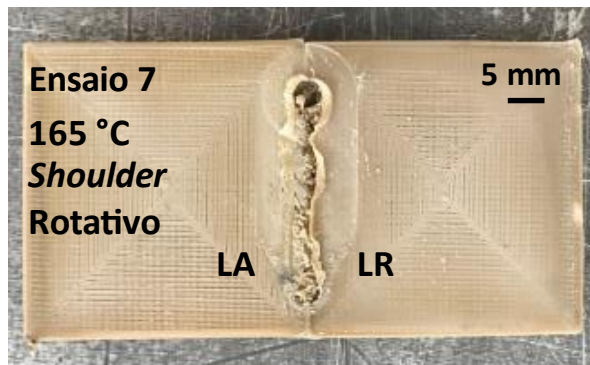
Aspeto visual da superfície das placas soldadas de PEEK do ensaio 7.
